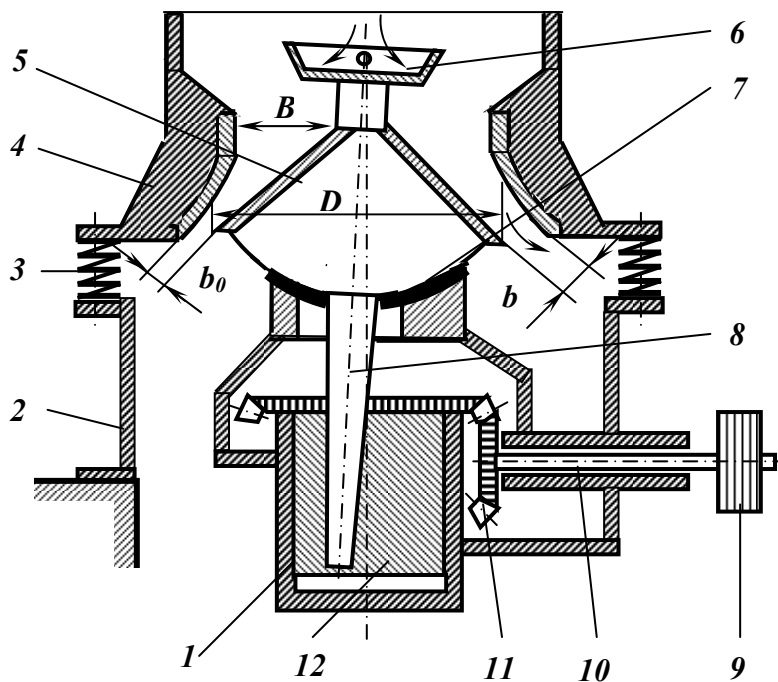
Схема конусної дробарки середнього і дрібного дроблення.
